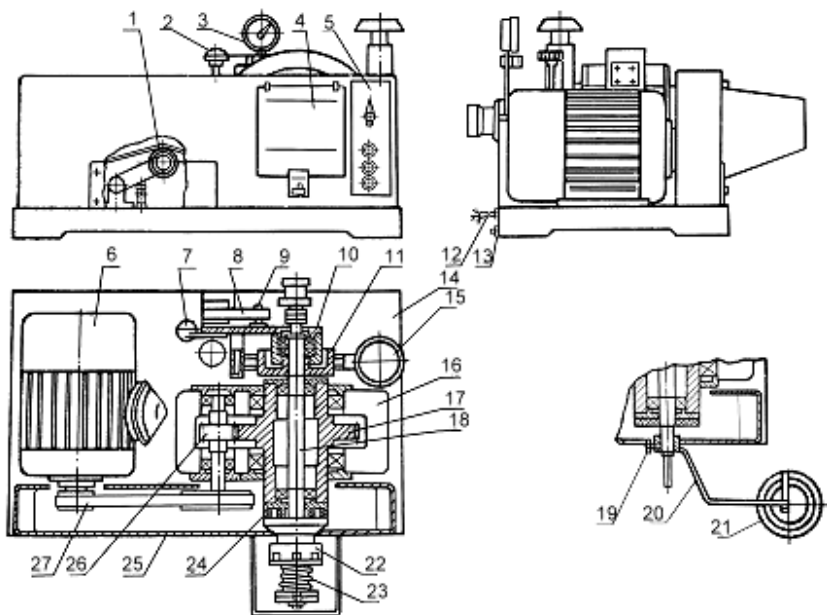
Установка ДМ-40 для испытания предохранительных муфт:
